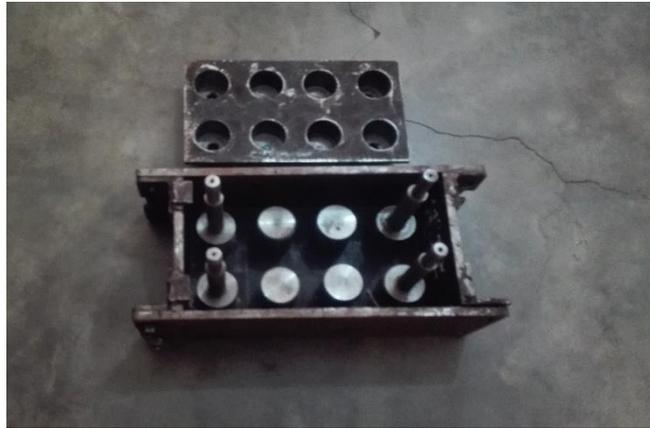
Desmoldante al molde 10.45 código de la plancha.
